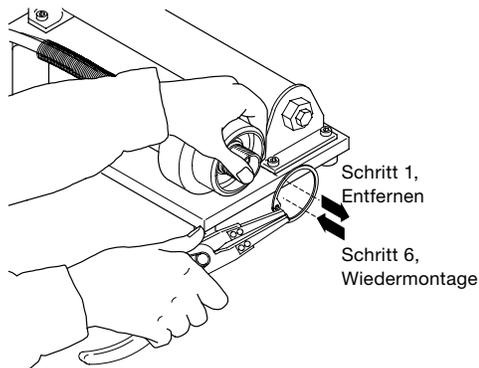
Entfernen/Wiedereinsetzen des Sprengrings
